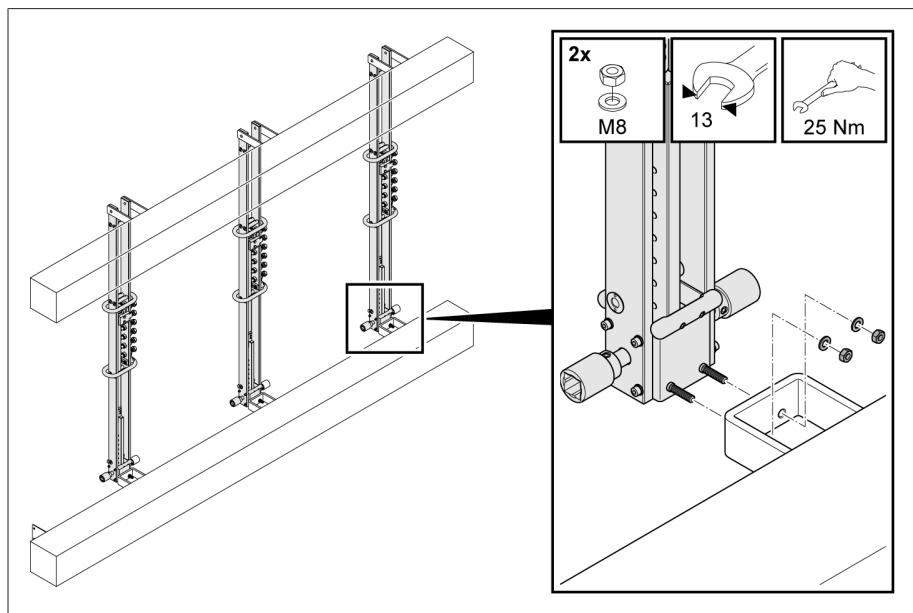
Крепление верхнего редуктора, устройство ПБВ с боковым расположением контактов
